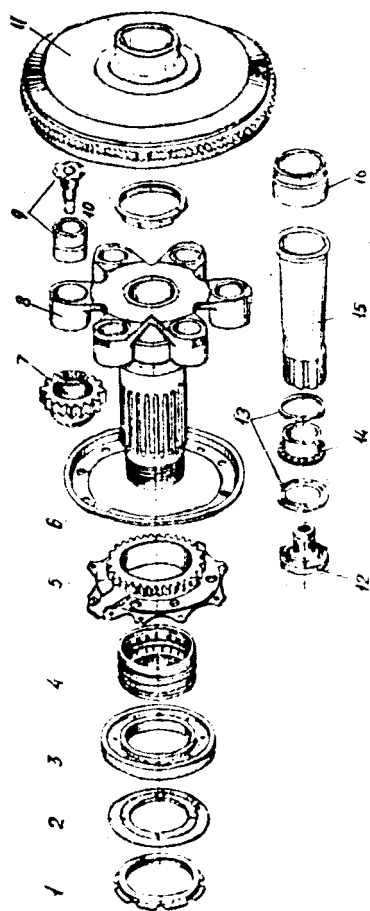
Детали редуктора: 1 — гайка упорного подшипника вала винта; 2 — маслоотражатель; 3 — опорно-упорный подшипник; 4 — распорная втулка подшипника; 5 — подшипник шестерни; 6 — предохранительное кольцо сателлитов; 7 — сателлит; 8 — вал винта, 9 — втулка и гайка сателлитов; 10 — гайка крепления ведущей шестерни; 11 — ведущая шестерня; 12 — маслораспределительная втулка; 13 — прокладка; 14 — передняя втулка вала винта; 15 — гильза вала винта; 16 — задняя втулка вала винта
